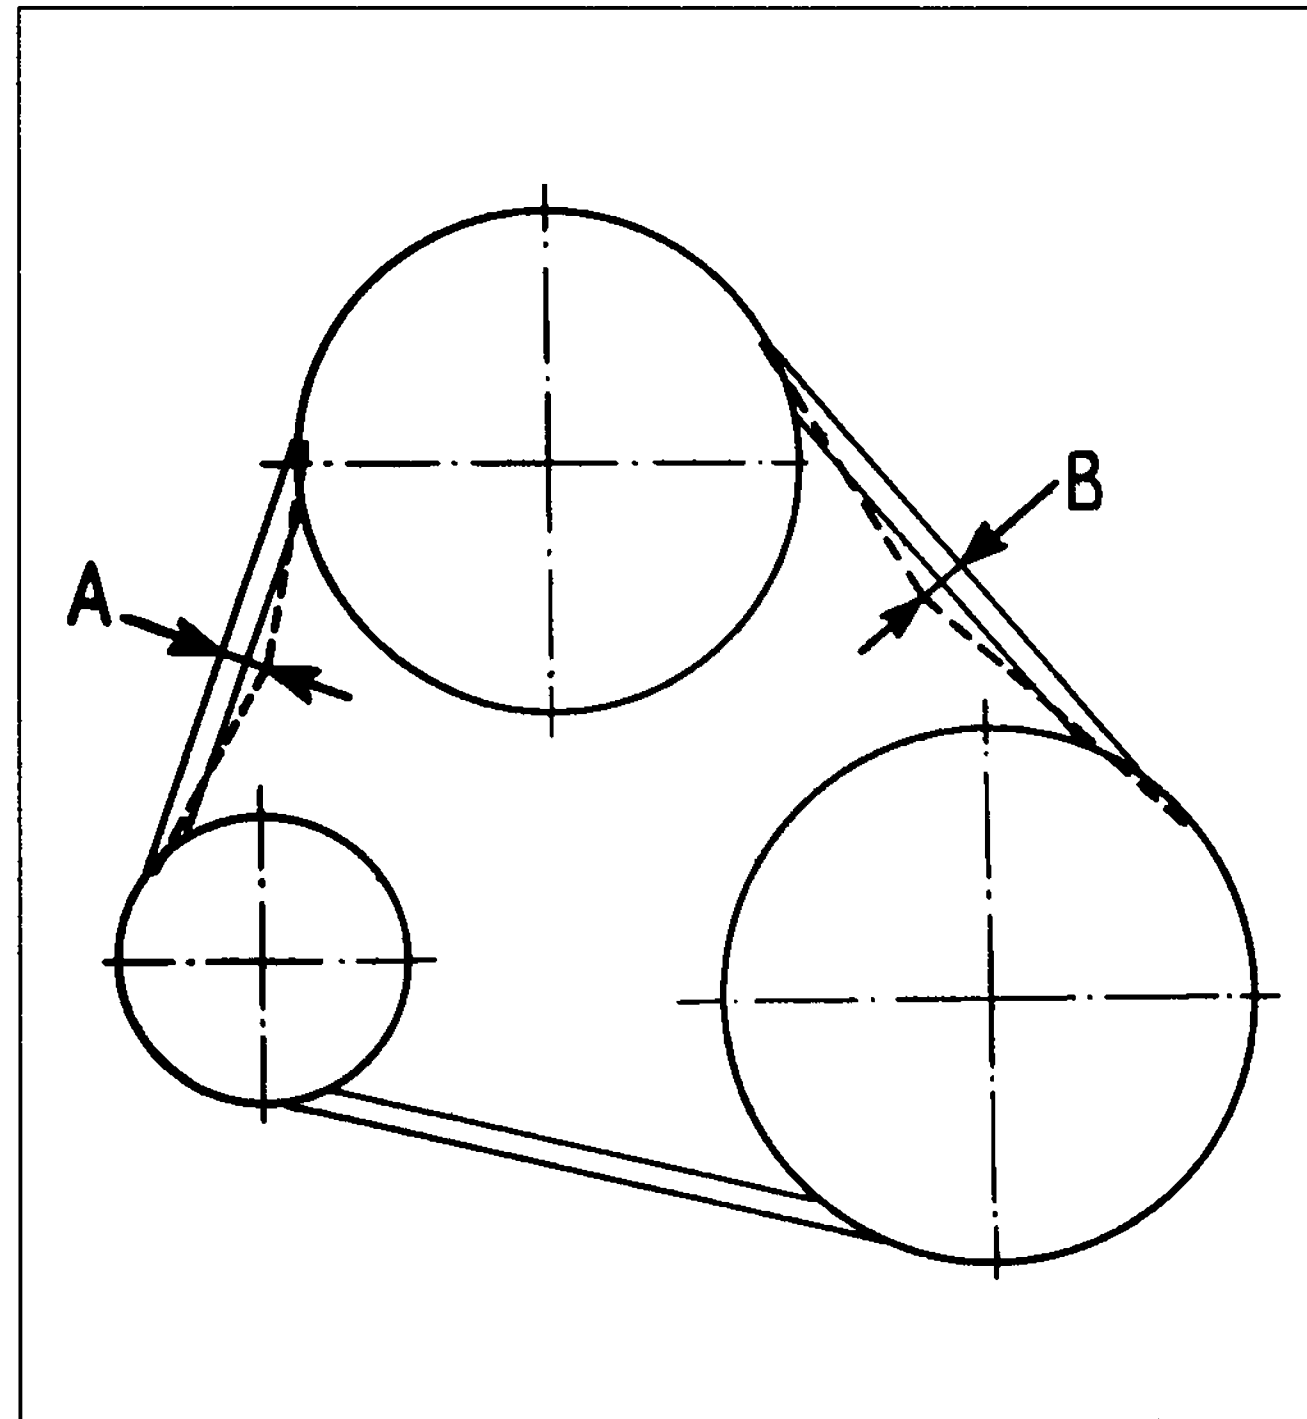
Схема проверки натяжения ремня привода насоса
